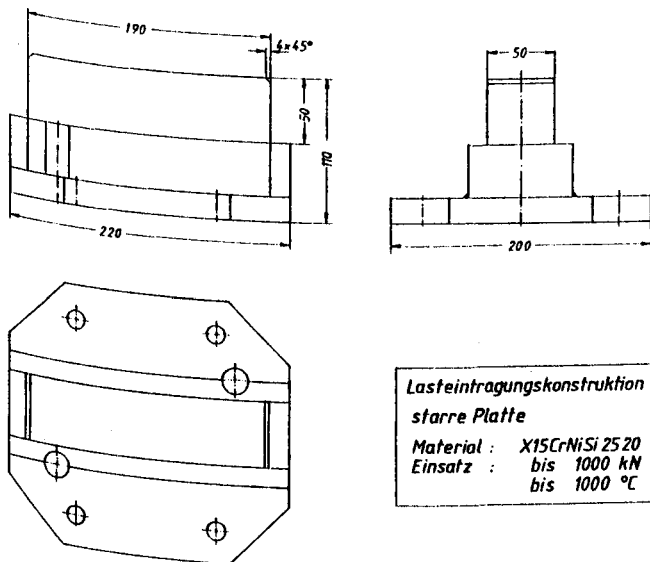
Lasteintragungskonstruktion: starre Platte
